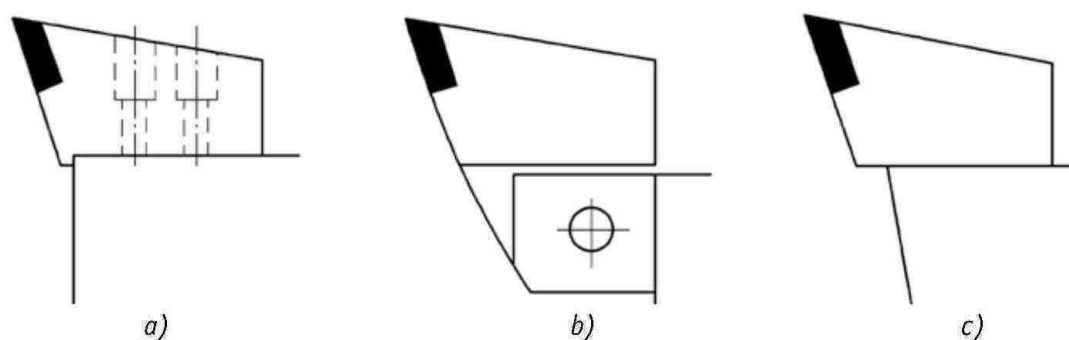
Способы крепления резка в проходческих щитах: а) болтовое; б) шпоночное; с) сварное
